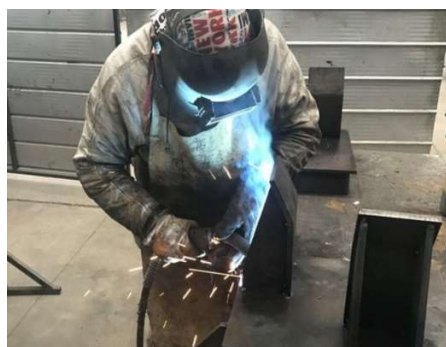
Trabajos en soldadura a gasa estructuras
